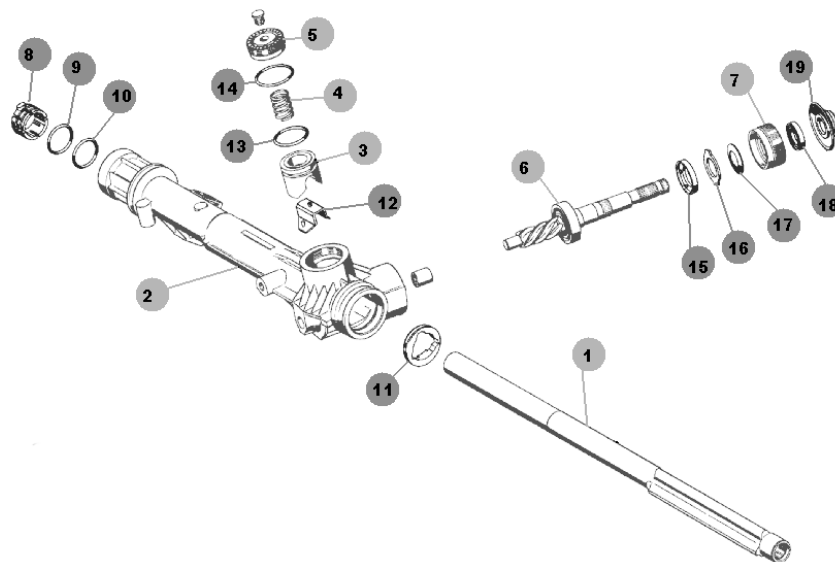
Механічна рульова рейка 1-й вигляд
